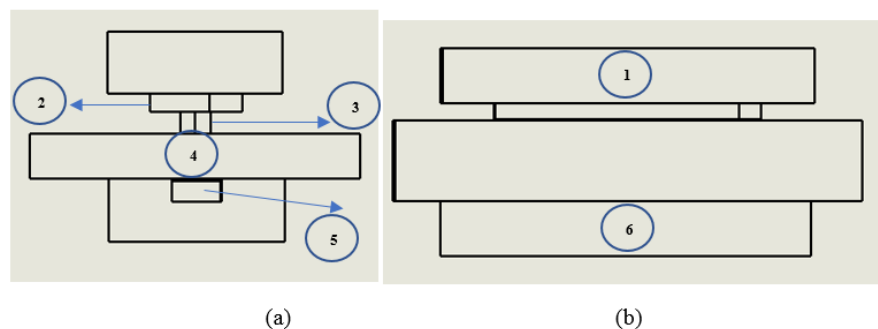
(a) Vista frontal del molde; (b) Vista Lateral del molde
